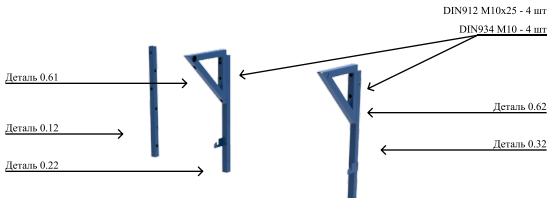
Сборка элементов верхней части стоек и оснований турника
